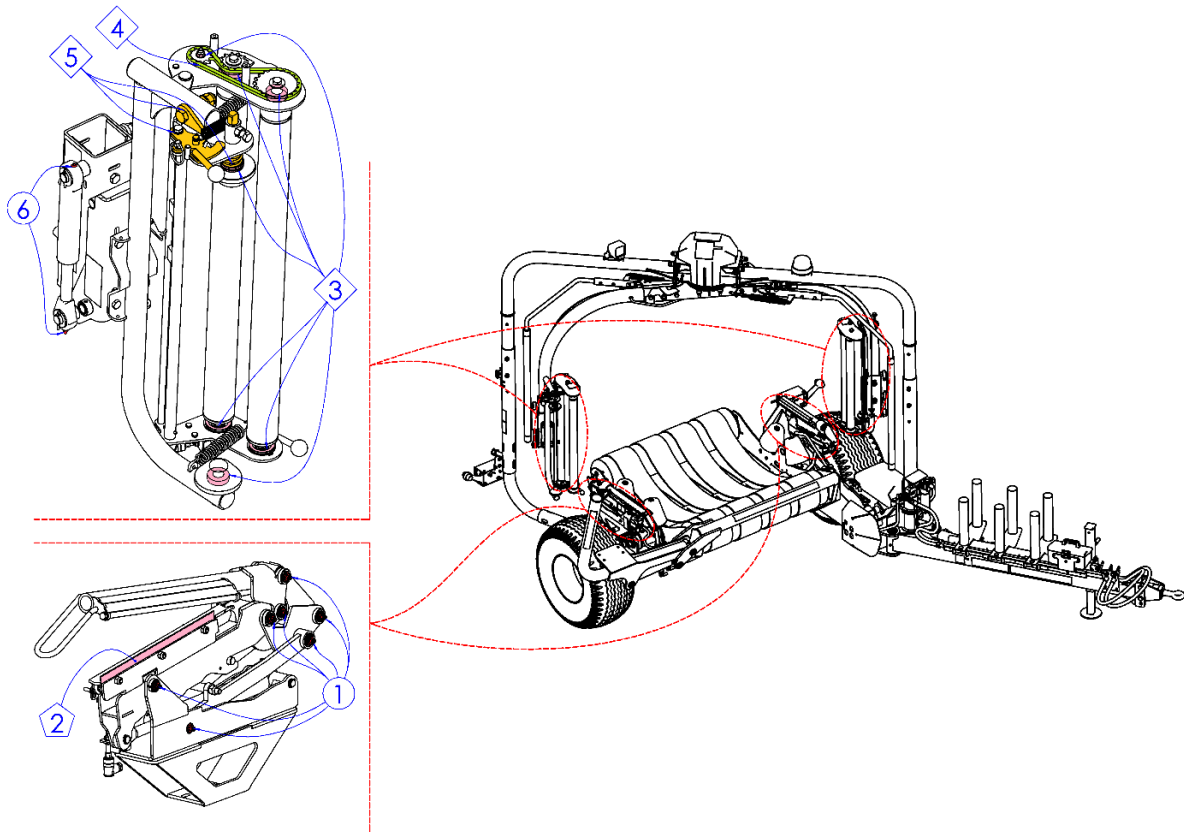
Точки смазки обрезчика пленки и подавателя пленки:
